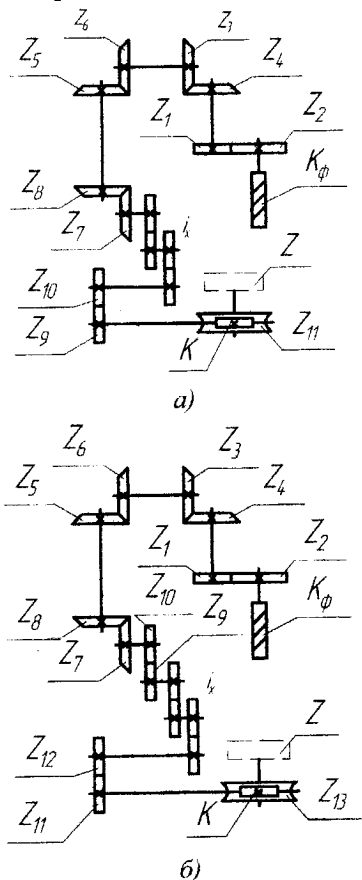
Кінематичні ланцюги обкату (ділення) зубофрезерного верстата
